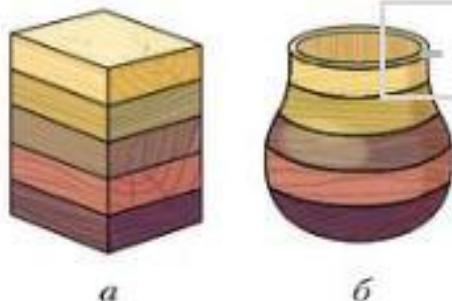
Блокная заготовка (а) и готовое изделие (б)
